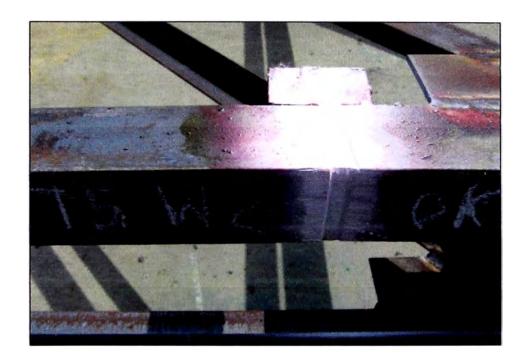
Inspección de pase raíz en tijeral T-5, soldador w2.
